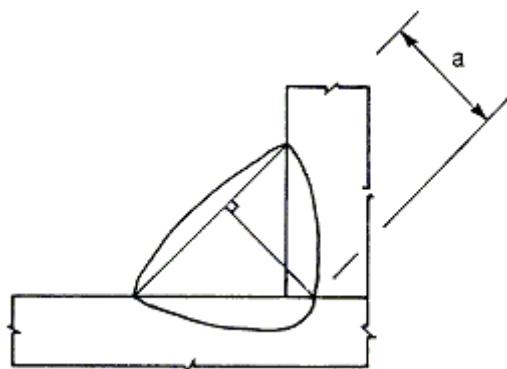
Толщина углового сварного шва с полным проваром
